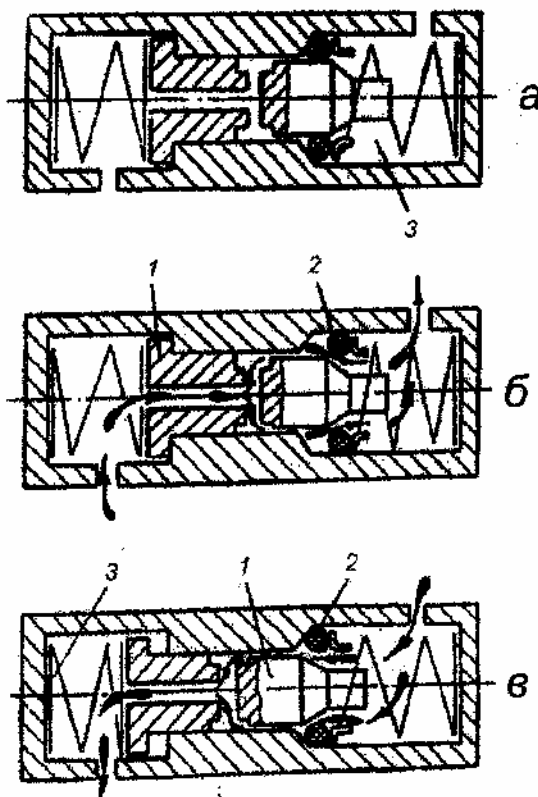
Схема работы подпорного клапана: а - нейтральное положение; б - нагнетание жидкости в гидроцилиндр; в - слив жидкости из гидроцилиндра; 1 - шток; 2 - кольцо уплотнительное; 3 - пружина
